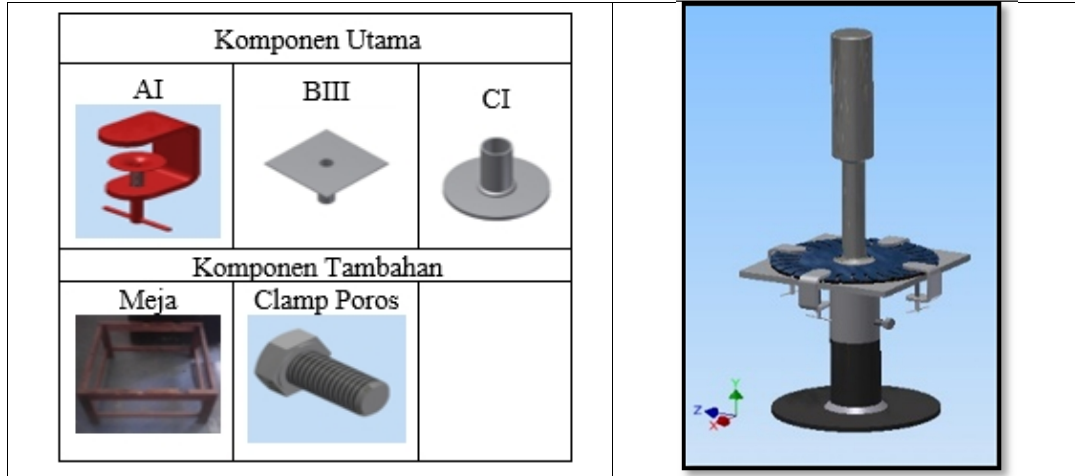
Alternatif ke-1 *assembly fixture* perakitan *runner*.
